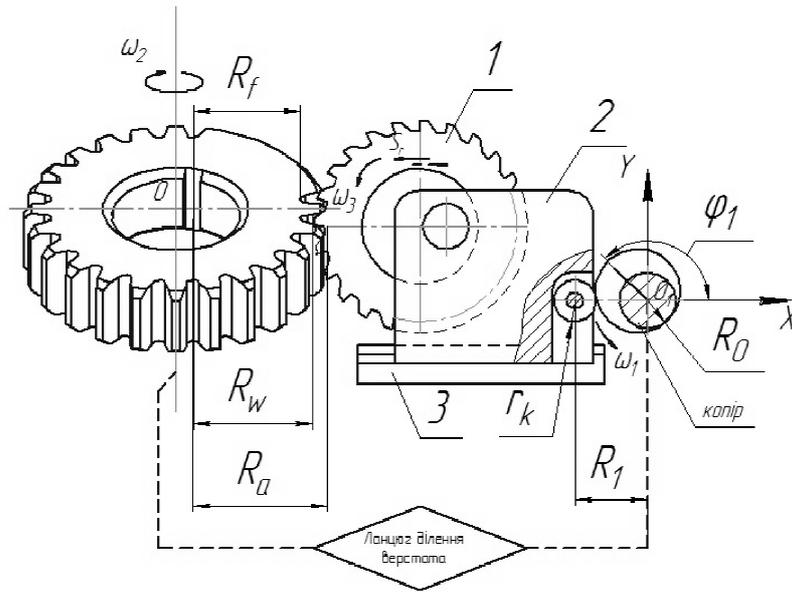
Схема нарізання зубців глобоїдального черв'ячного колеса способом РКБД за допомогою копіювального пристрою.
